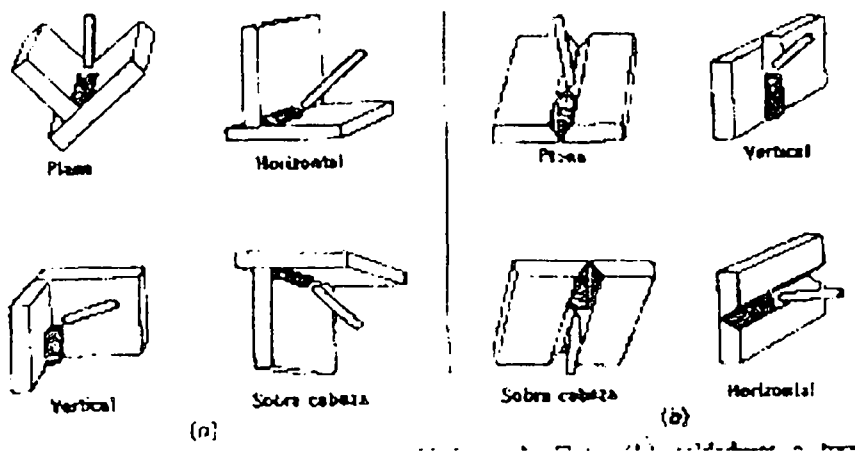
Posiciones para soldar (a) Soldadura de filete (b) Soldadura a tope.
